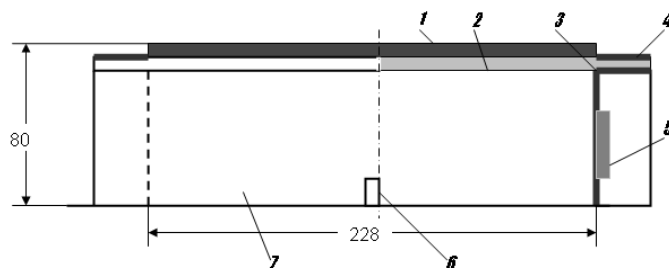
Схема безззорного ковпака ковзуна ТАУС
